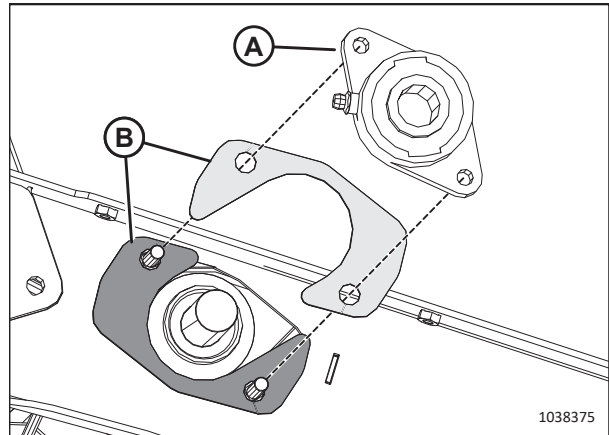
Підшипник приводного ролика полотняного транспортера
